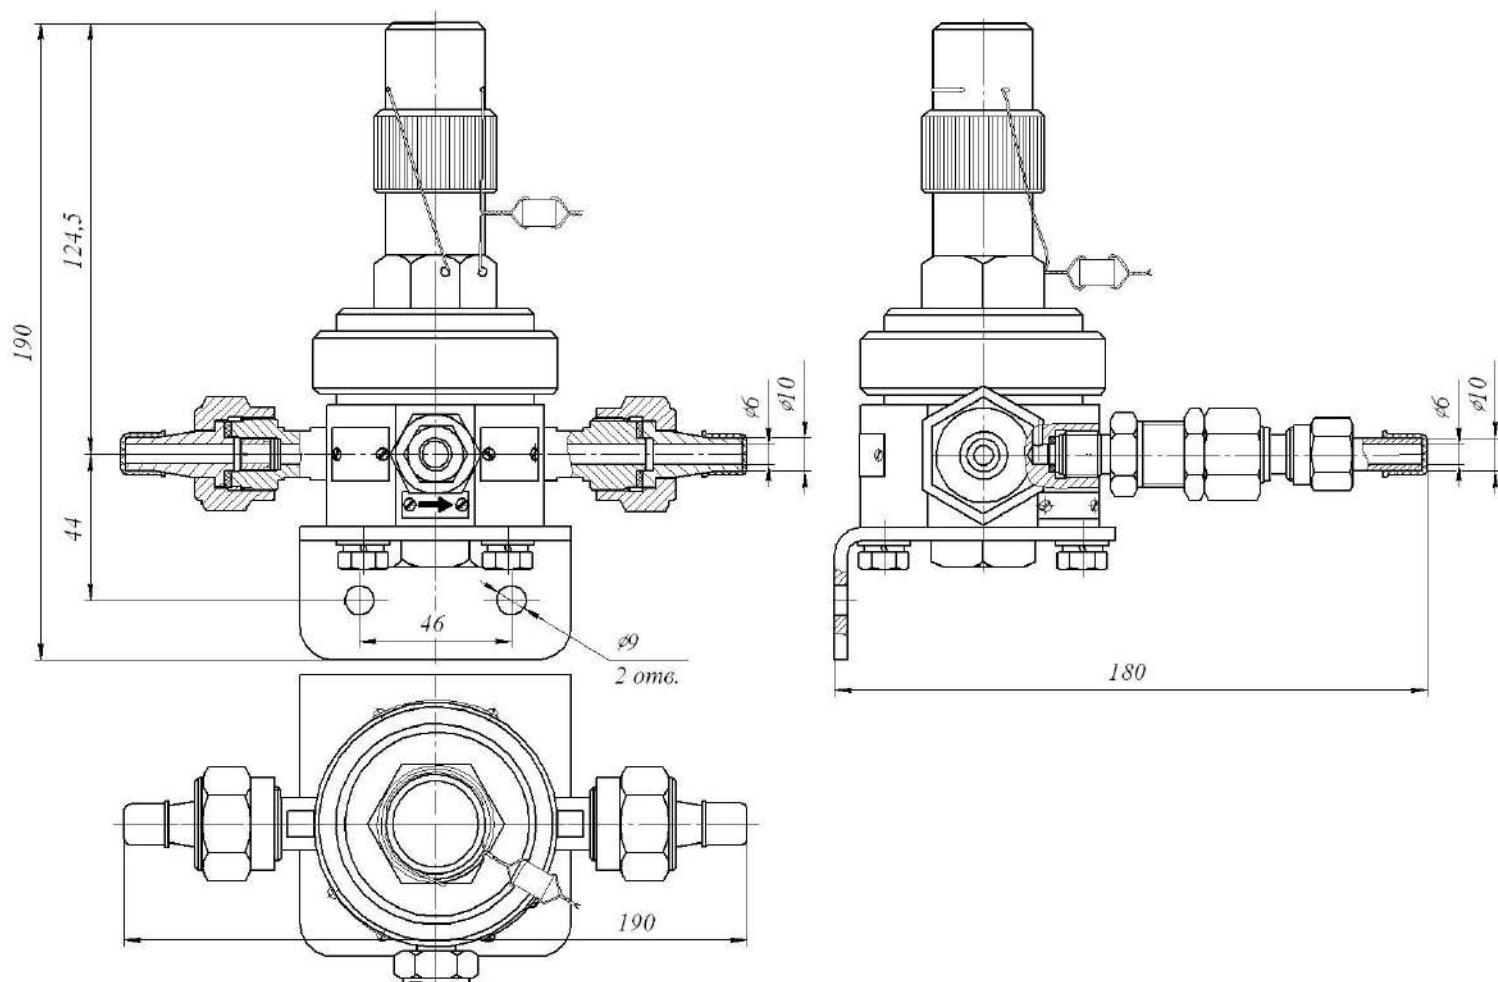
Габаритные и присоединительные размеры РДФ-7-13
